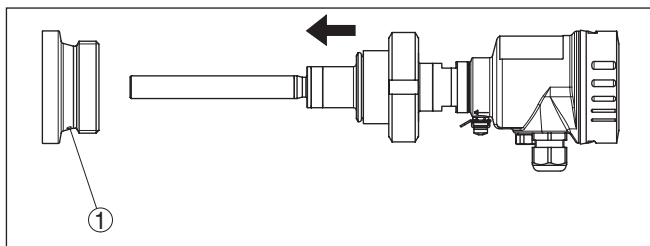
Montaje interruptor de nivel vibratorio en el racor soldado
